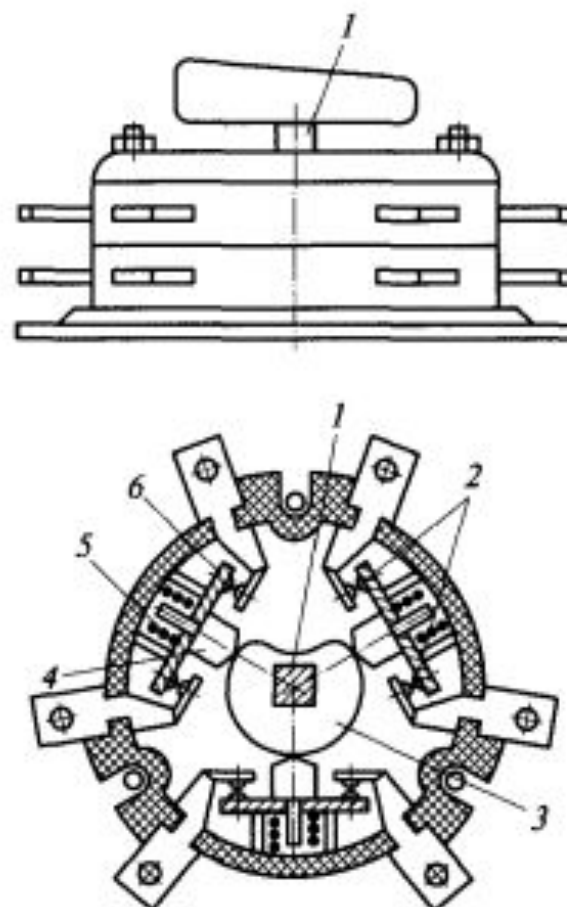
Пакетный кулачковый выключатель серии ПКВ:
